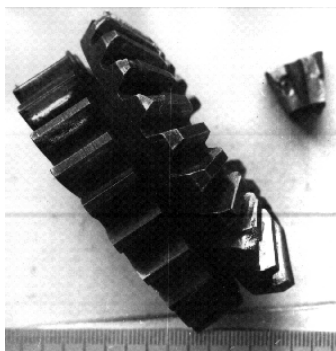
Общий вид разрушенной шестерни распредвала двигателя ЗД6
